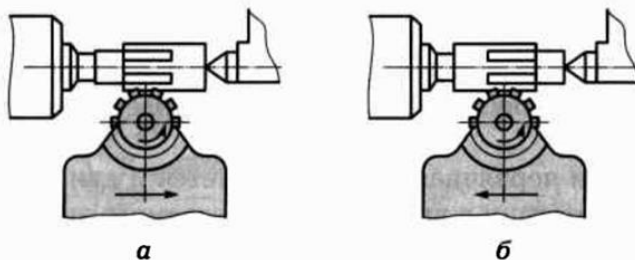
Схема попутного (а) та зустрічного фрезерування
